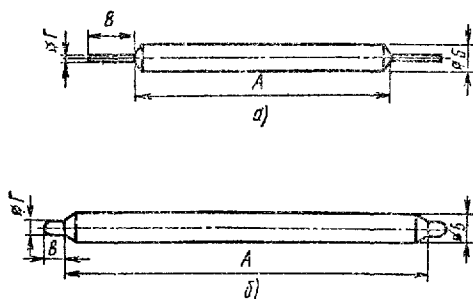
Общий вид, габаритные и присоединительные размеры выпрямительных столбов и блоков:
